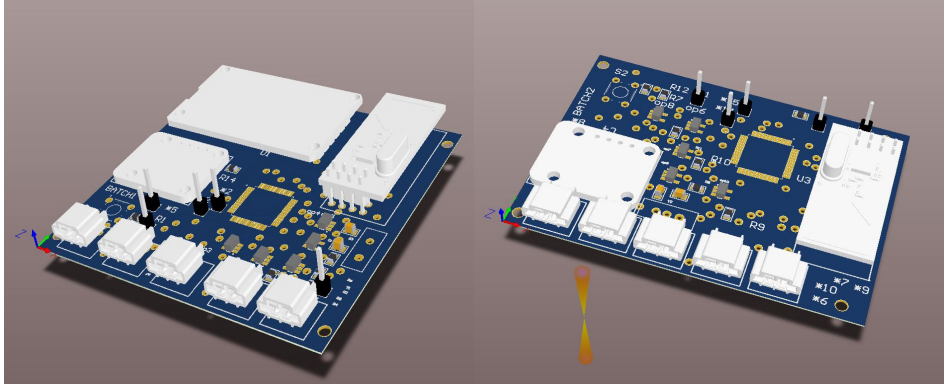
Izquierda:PCB placa maestra, derecha: PCB placa esclava
